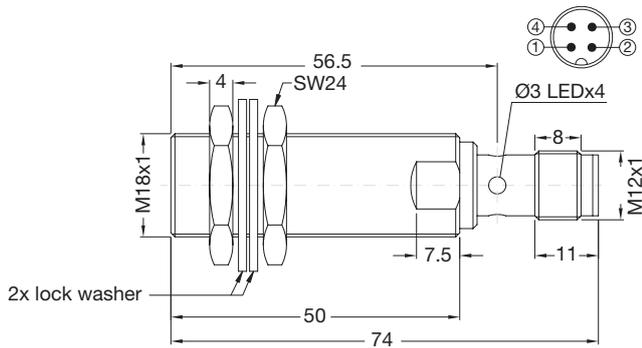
Lange Ausführung, bündiger Einbau, Steckversion
